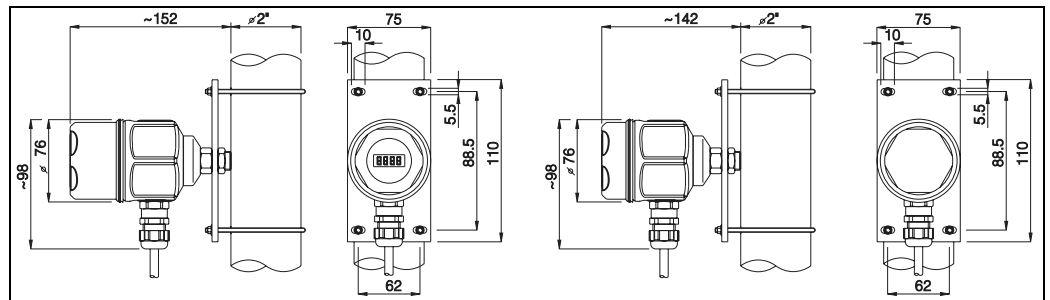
Gesamtabmessungen bei Rohrmontage (in mm)
